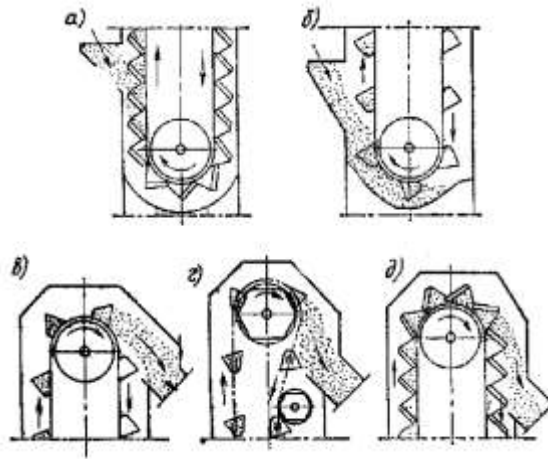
Схемы загрузки и разгрузки ковшового элеватора:
